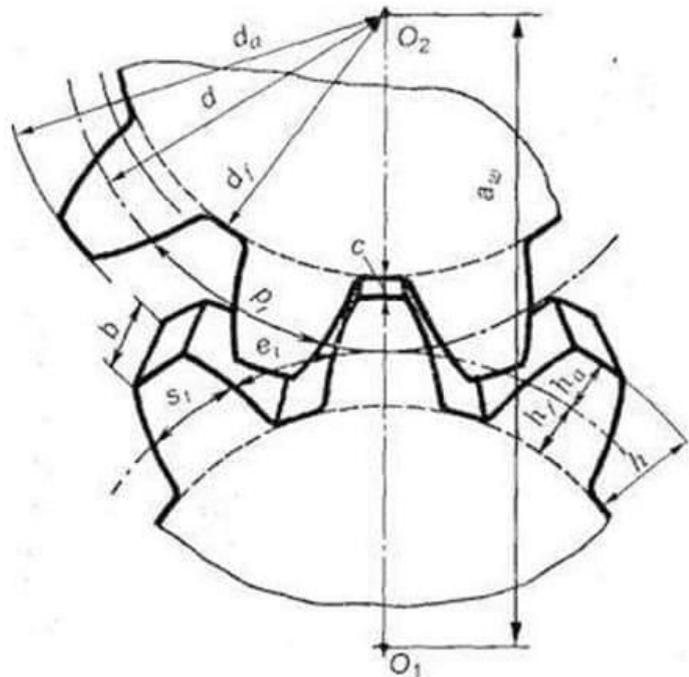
Основные параметры для расчета размеров зубчатых колес
